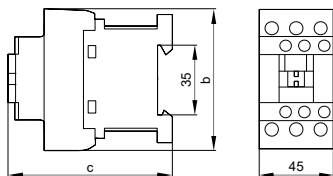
Габаритные размеры контакторов КМИ-А-22512, КМИ-А-23512 / Figure 2 — Overall dimensions of contactors KMI-A-22512, KMI-A-23512
